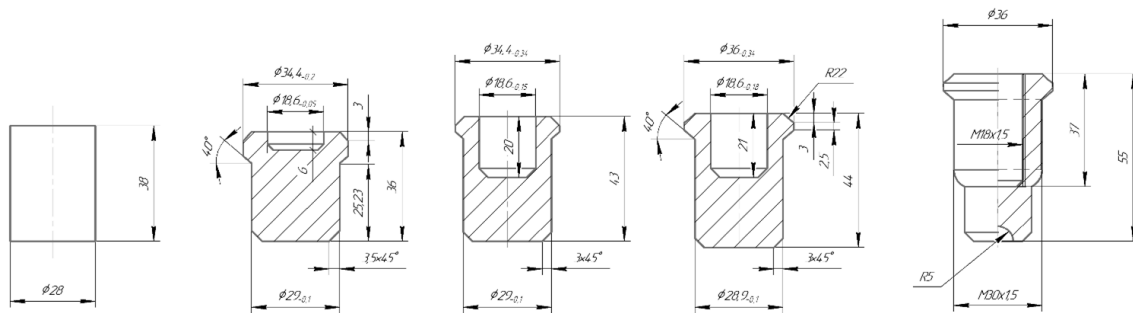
Предложенный вариант изготовления колпачковой гайки
